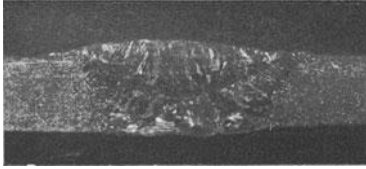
Makroschliff einer mit der Schlauchelektrode hergestellten Kupferschweiße.
